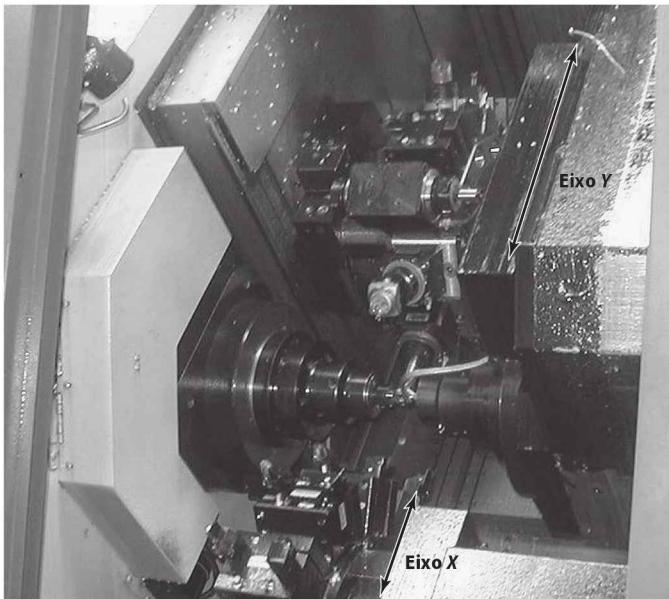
Este centro de torneamento CNC possui um eixo Y para permitir operações de fresagem em curva.
